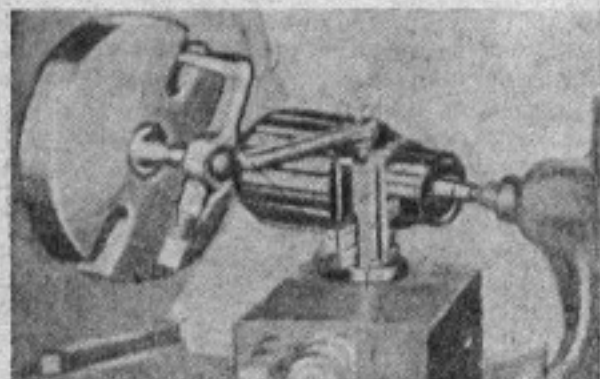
Установка якоря (генератора) в станке для проточки коллектора
